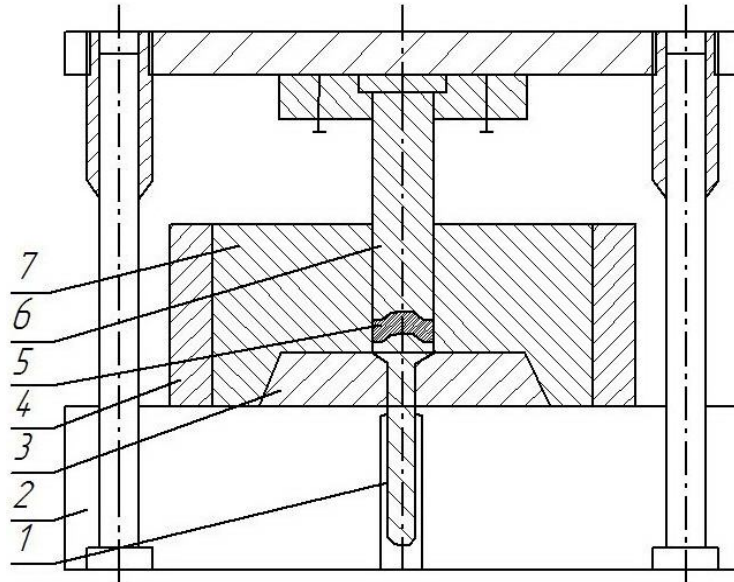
Схема штампа для гарячого видавлювання алюмінієвого прутка: 1 – пруток, що видавлюється; 2 – плита; 3 – вставка; 4 – обойма; 5 – заготовка; 6 – пуансон; 7 – матриця
